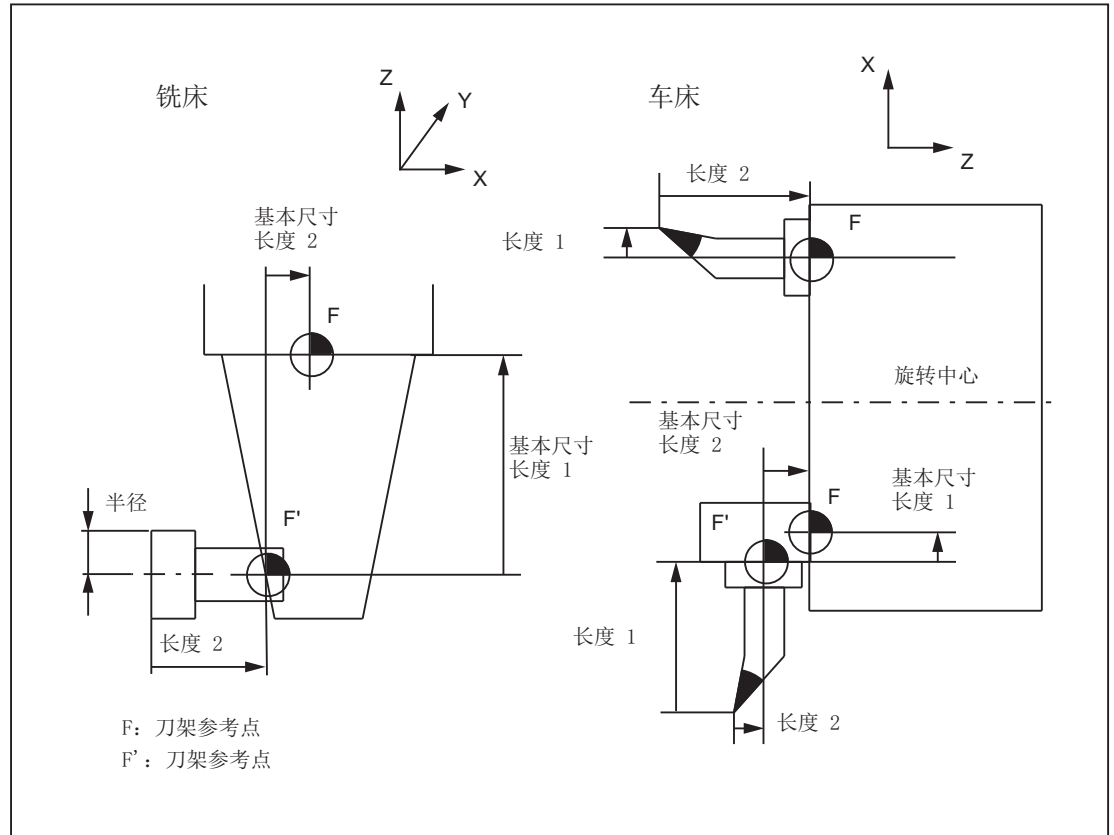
“基本尺寸/适配器尺寸 - 刀具长度补偿”的应用示例
